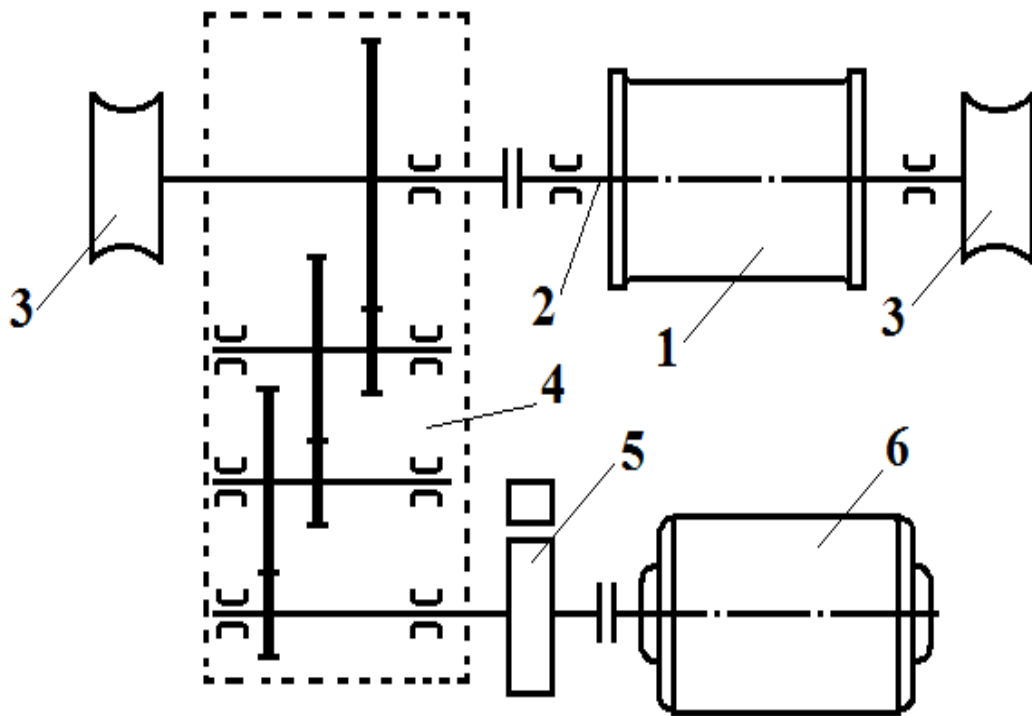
Кінематична схема лебідки з зубчатою передачею
